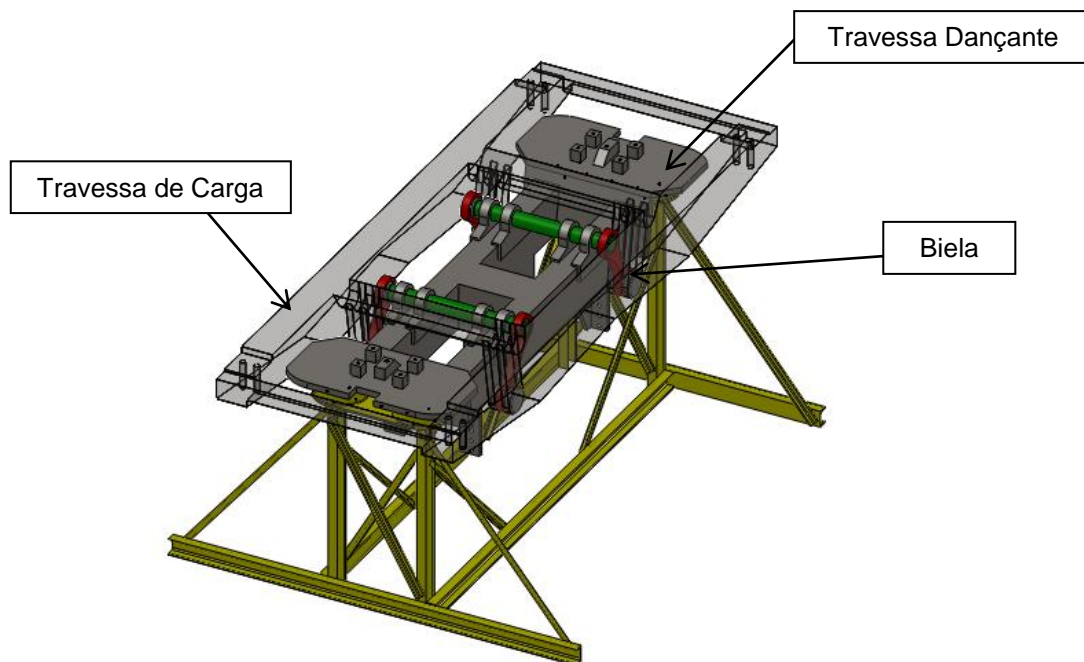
Estrutura com o conjunto Travessa de Carga/Travessa Dançante
